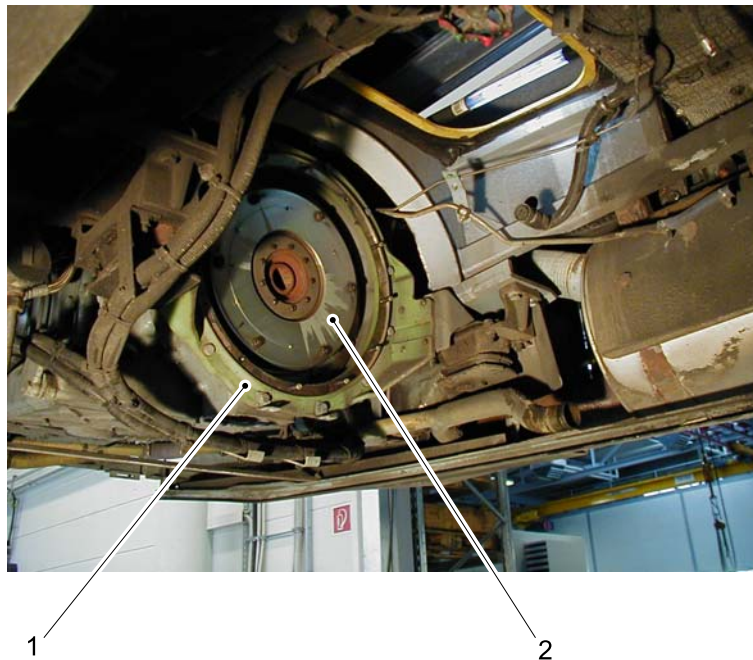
1 – Aufhängeflansch, 2 - Hydrodamp
